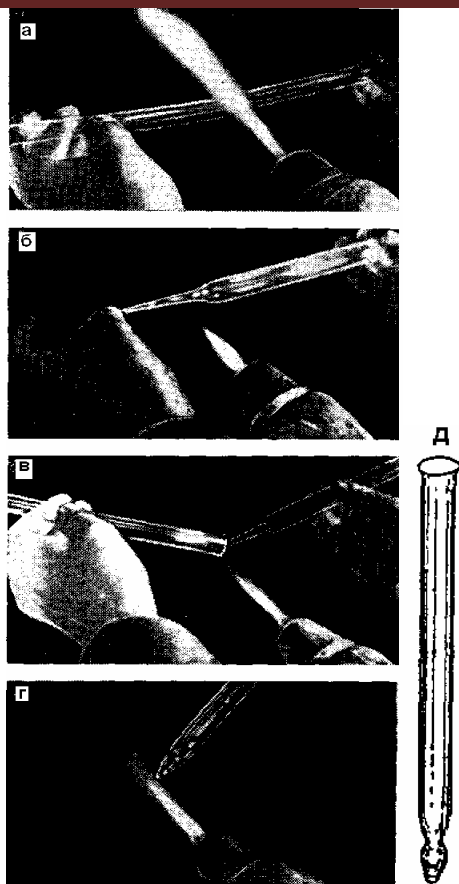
Изготовление заготовки бюретки без крана: а—приготовление заготовки; б—формирование оливки на одном конце; в—оплавление и развертывание второго конца; г—оплавление и отжиг конца бюретки; д—готовое изделие.
